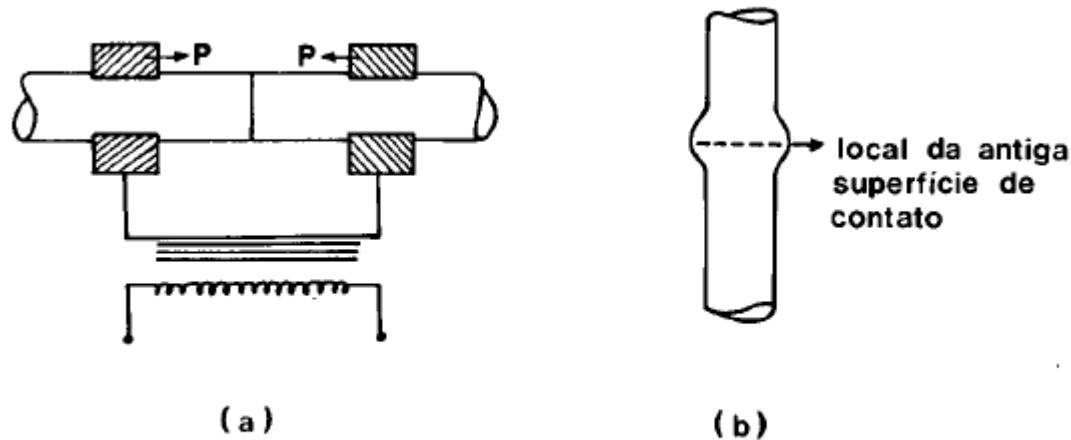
a) Esquema da soldagem topo-a-topo por resistência pura. b) aspecto da solda terminada
